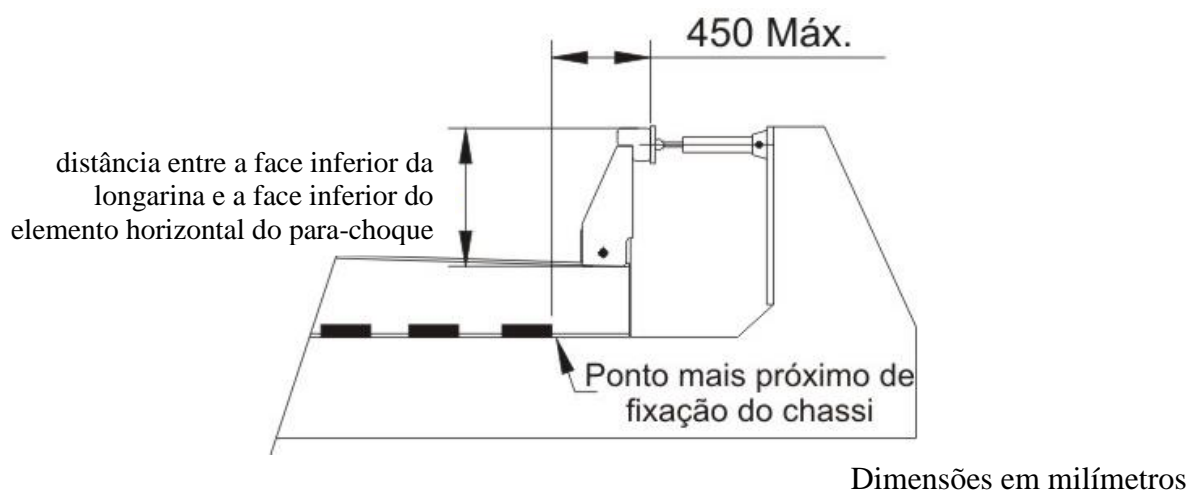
Exemplo de dispositivo de ensaio - Vista lateral
